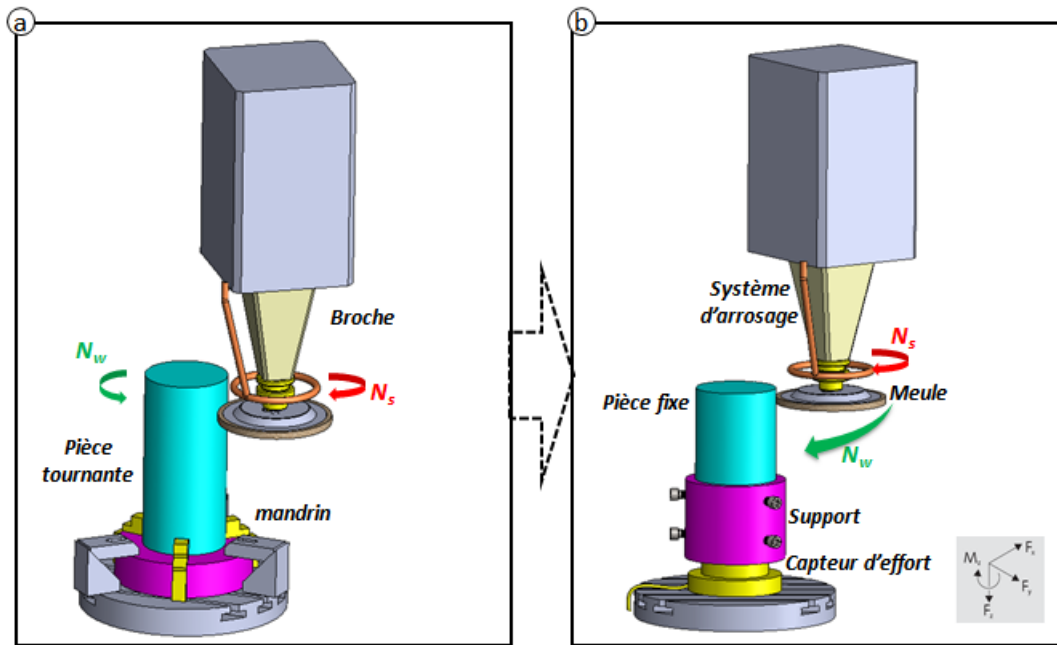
Vue d'ensemble de: (a) montage original ; (b) montage modifié pour la mesure des efforts
